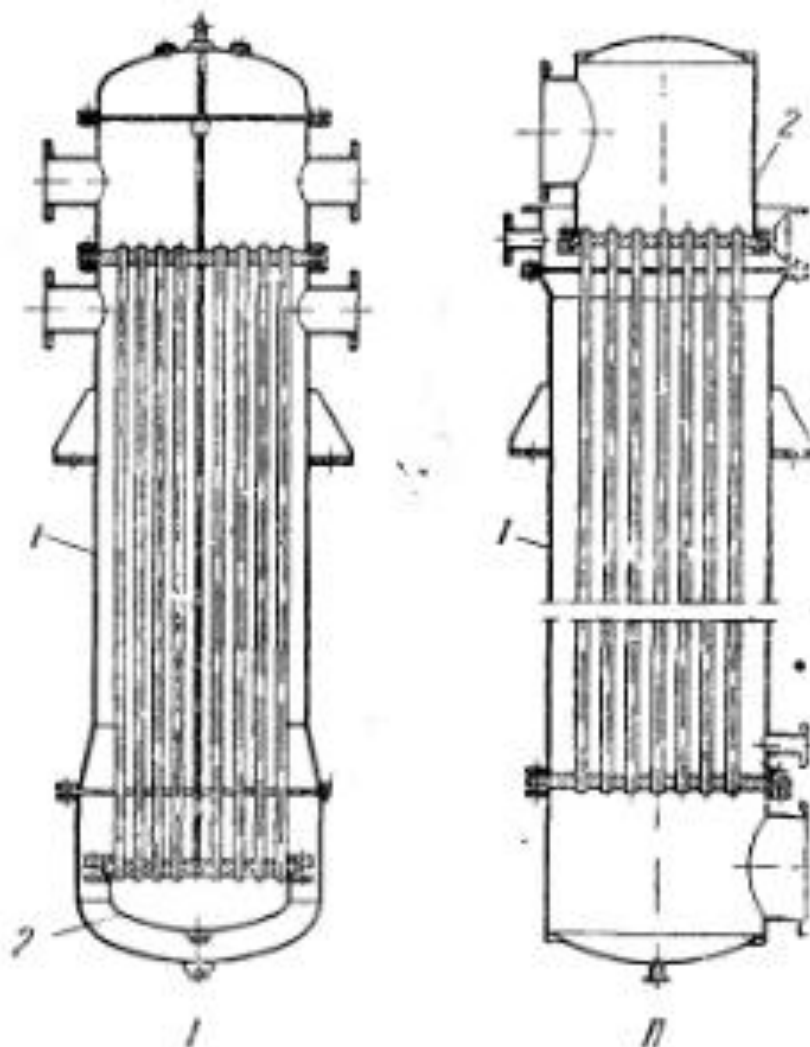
Теплообменники с «плавающей» головкой: I—закрытого типа; II—открытого типа, 1—кожух; 2—плавающая головка.
